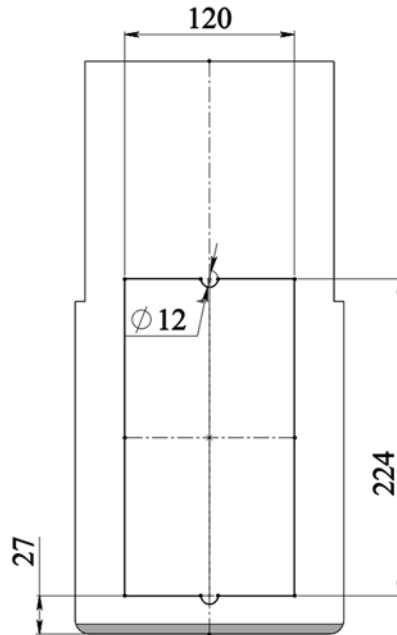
Эскиз выреза для пластин рессоры
